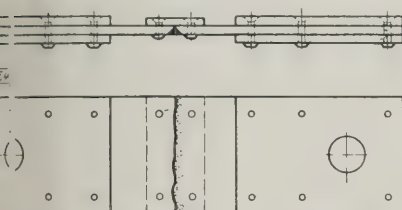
Verlaschter Stoß; Stoß senkrecht geschweißt.
